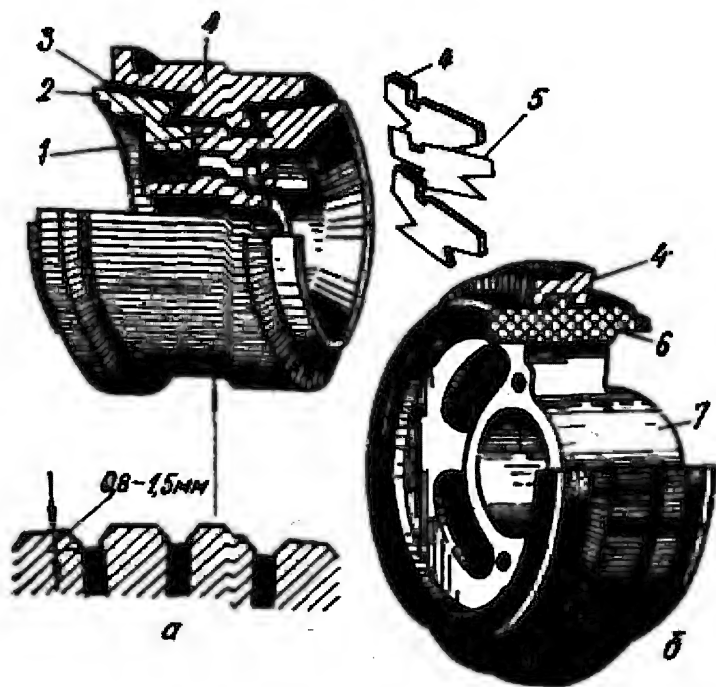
Коллекторы с металлическим (а) и пластмассовым (б) корпусами
